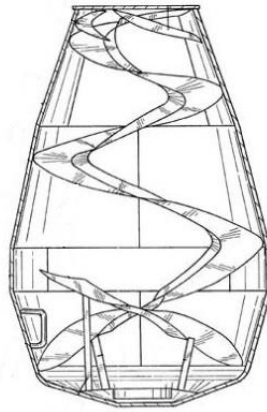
Corte en planta del tambor mezclador.⁶¹
